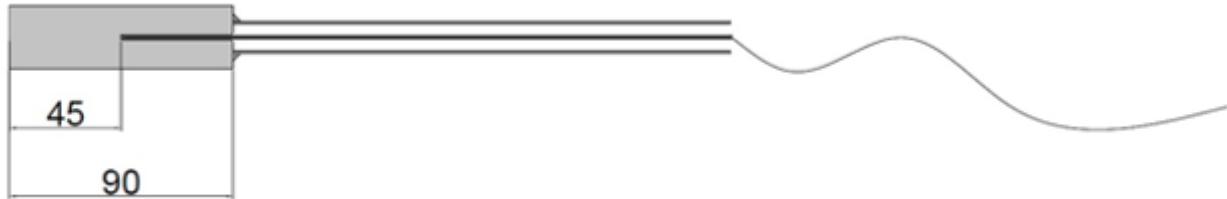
Corte esquemático de una de las probetas con tubo soldado por el que pasa la termocupla (valores en mm)
